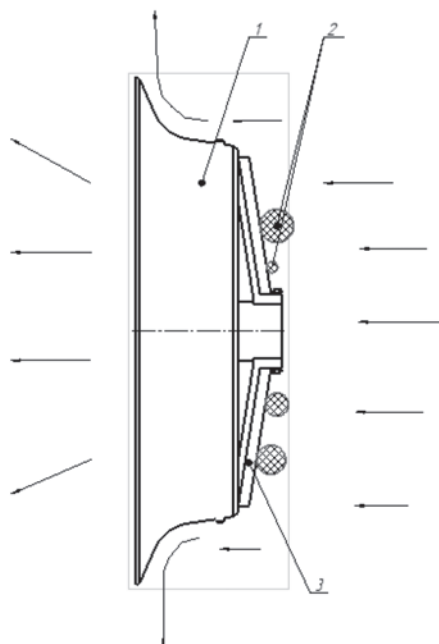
Схема движения потоков навозной массы по кожуху: 1 – кожух; 2 – крупные комки навозной массы; 3 – стойка
